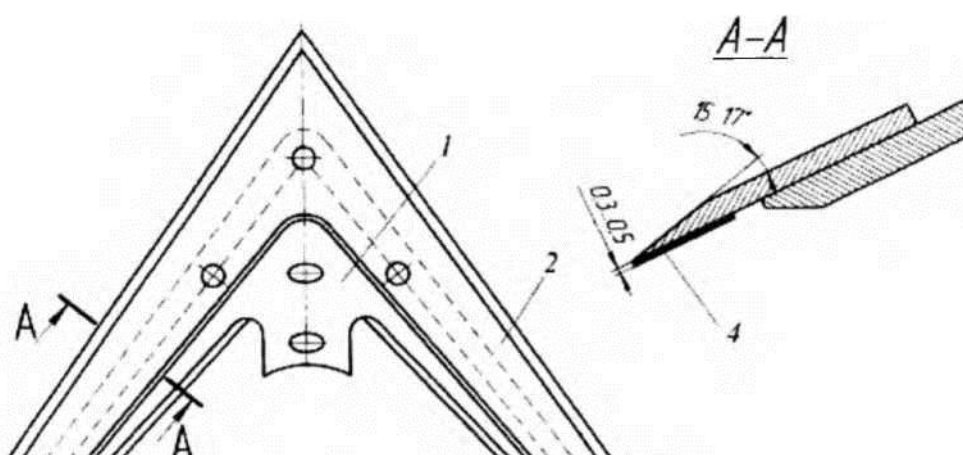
Робочий орган культиватора [17], вид зверху
